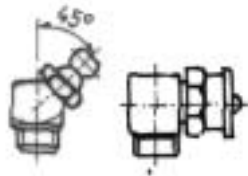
Piesă de poziție cu ungător: a-montare înclinată la 45°;
